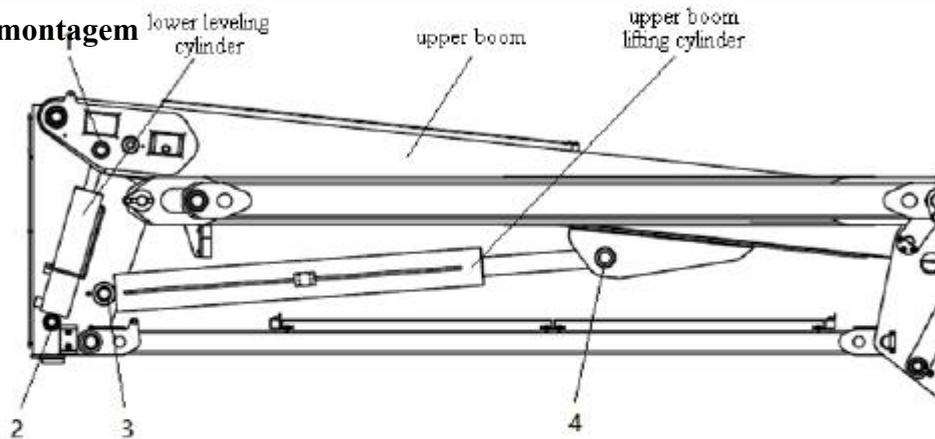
Diagrama de desmontagem do cilindro de elevação inferior e cilindro de elevação do braço
